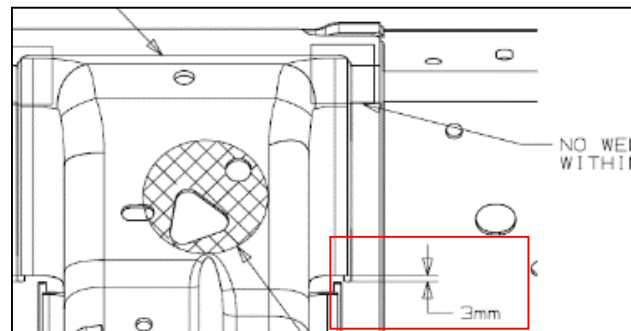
Soldadura fuera de junta. [14]
